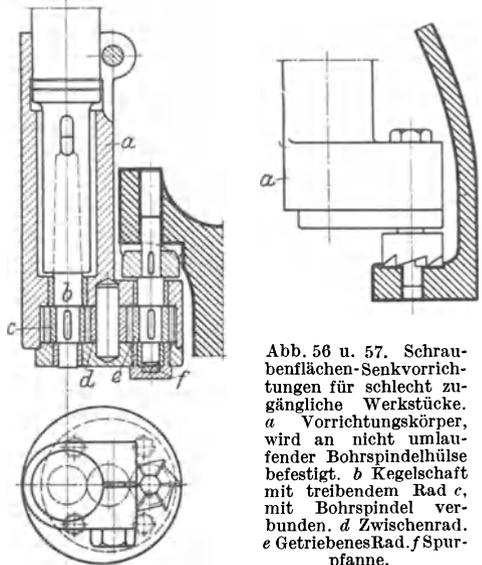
u. 57. Schraubenflächen-Senkvorrichtungen für schlecht zugängliche Werkstücke. *a* Vorrichtungskörper, wird an nicht umlaufender Bohrspindelhülse befestigt. *b* Kegelschaft mit treibendem Rad *c*, mit Bohrspindel verbunden. *d* Zwischenrad. *e* Getriebenes Rad. *f* Spurpfanne.
